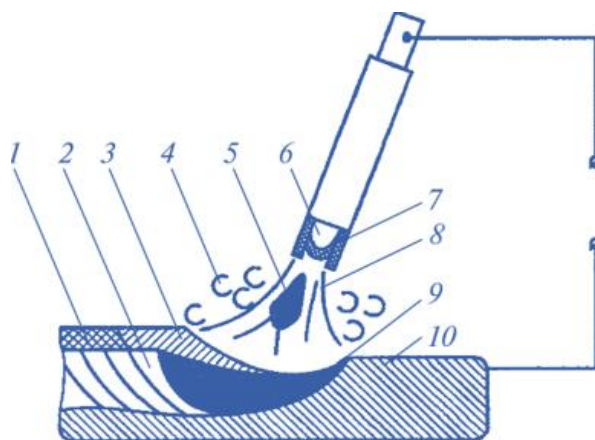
Схема процесса ручной дуговой сварки покрытым электродом: 1-твердый шлак; 2-шов; 3-жидкий шлак; 4-газовая защита; 5-капли жидкого металла; 6-стержень; 7-электродное покрытие; 8-дуга; 9-сварочная ванна; 10-деталь
